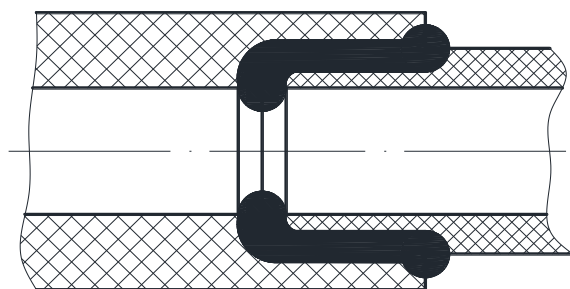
Конструктивные элементы шва сварного соединения (шов НС6)
